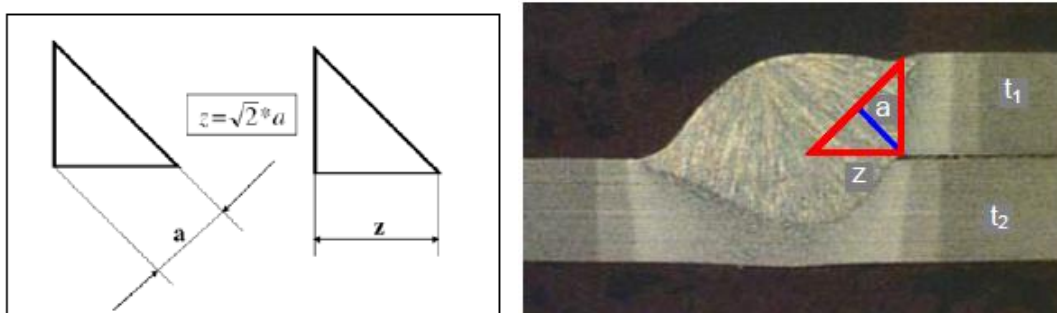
Ejemplo de medición de la altura de un cordón de soldadura. Fotografías extraídas de la especificación general de Ford sobre soldadura MAG ESBM5A-1B310-AA.
